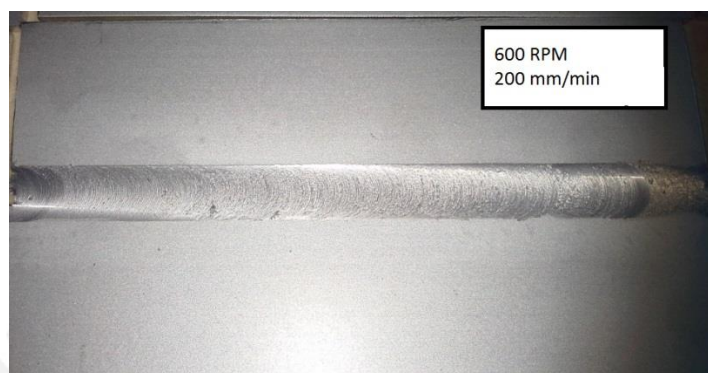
Canal de soldadura a 600RPM y 200 mm/min
